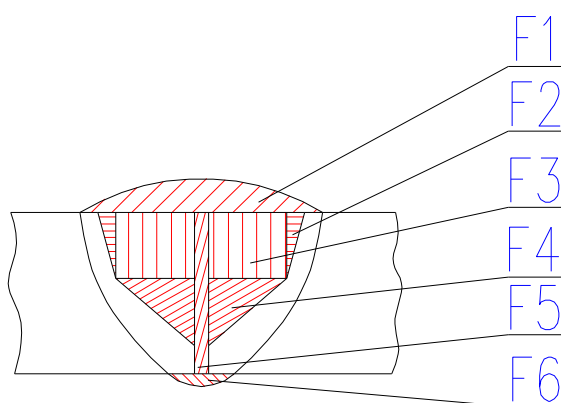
Соединение №1. Схема расчета поперечной площади.
